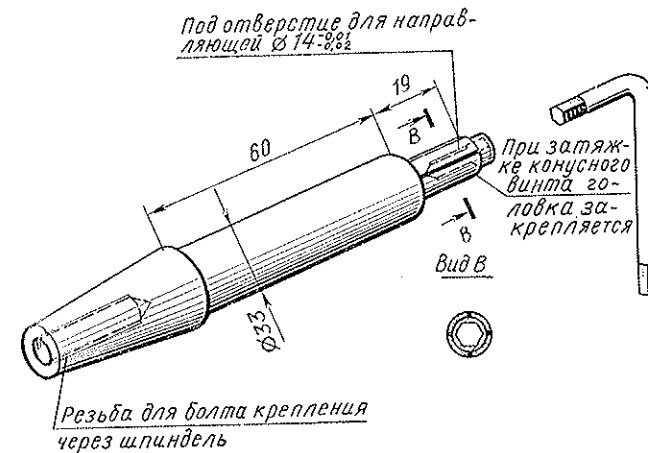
Приспособление для крепления головки при расточке гнезда под седло клапана на токарном станке.
